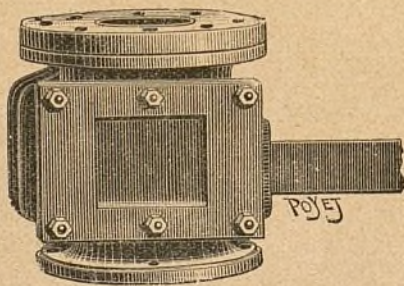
Válvula Barbe vista en parte por su parte exterior.
